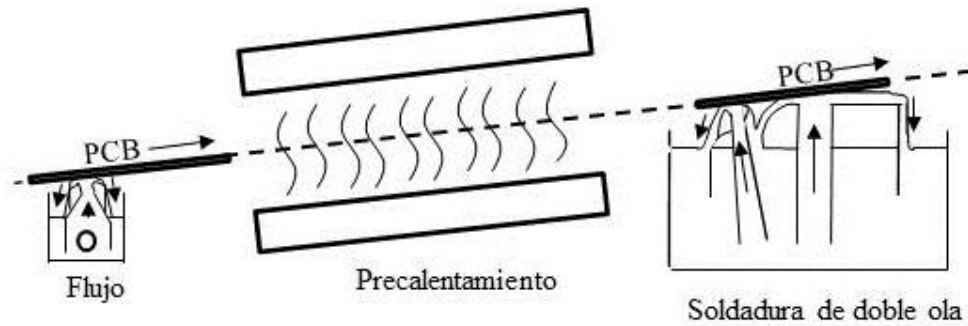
Proceso de soldadura de doble ola [2].
